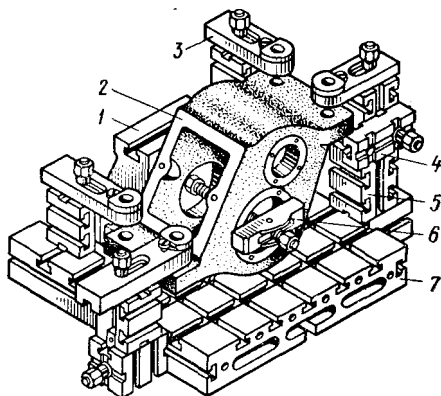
Приспособление УСП для сверления отверстий в корпусной детали
